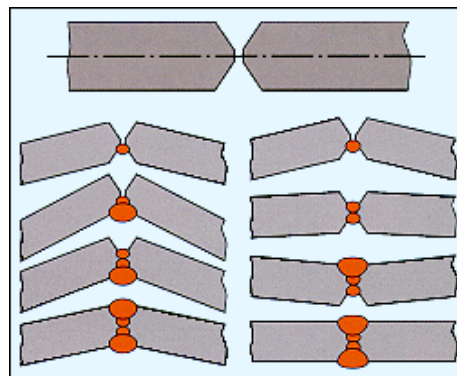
Soldadura equilibrada para reducir la cantidad de distorsión angular ²³
